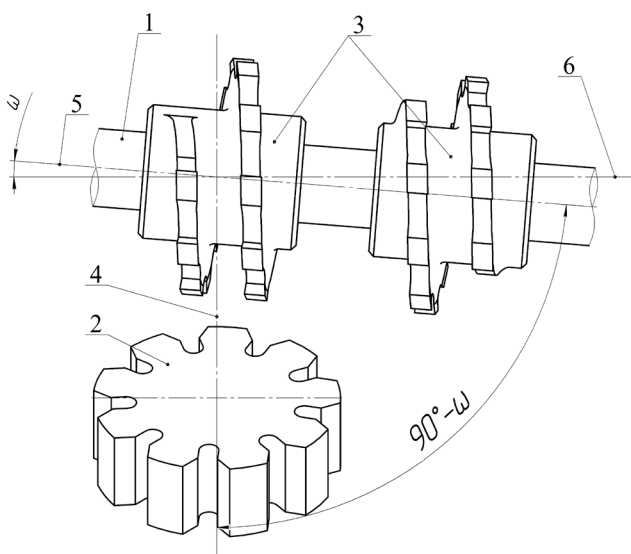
Схема установки фрези на кут підйому гвинтової лінії
